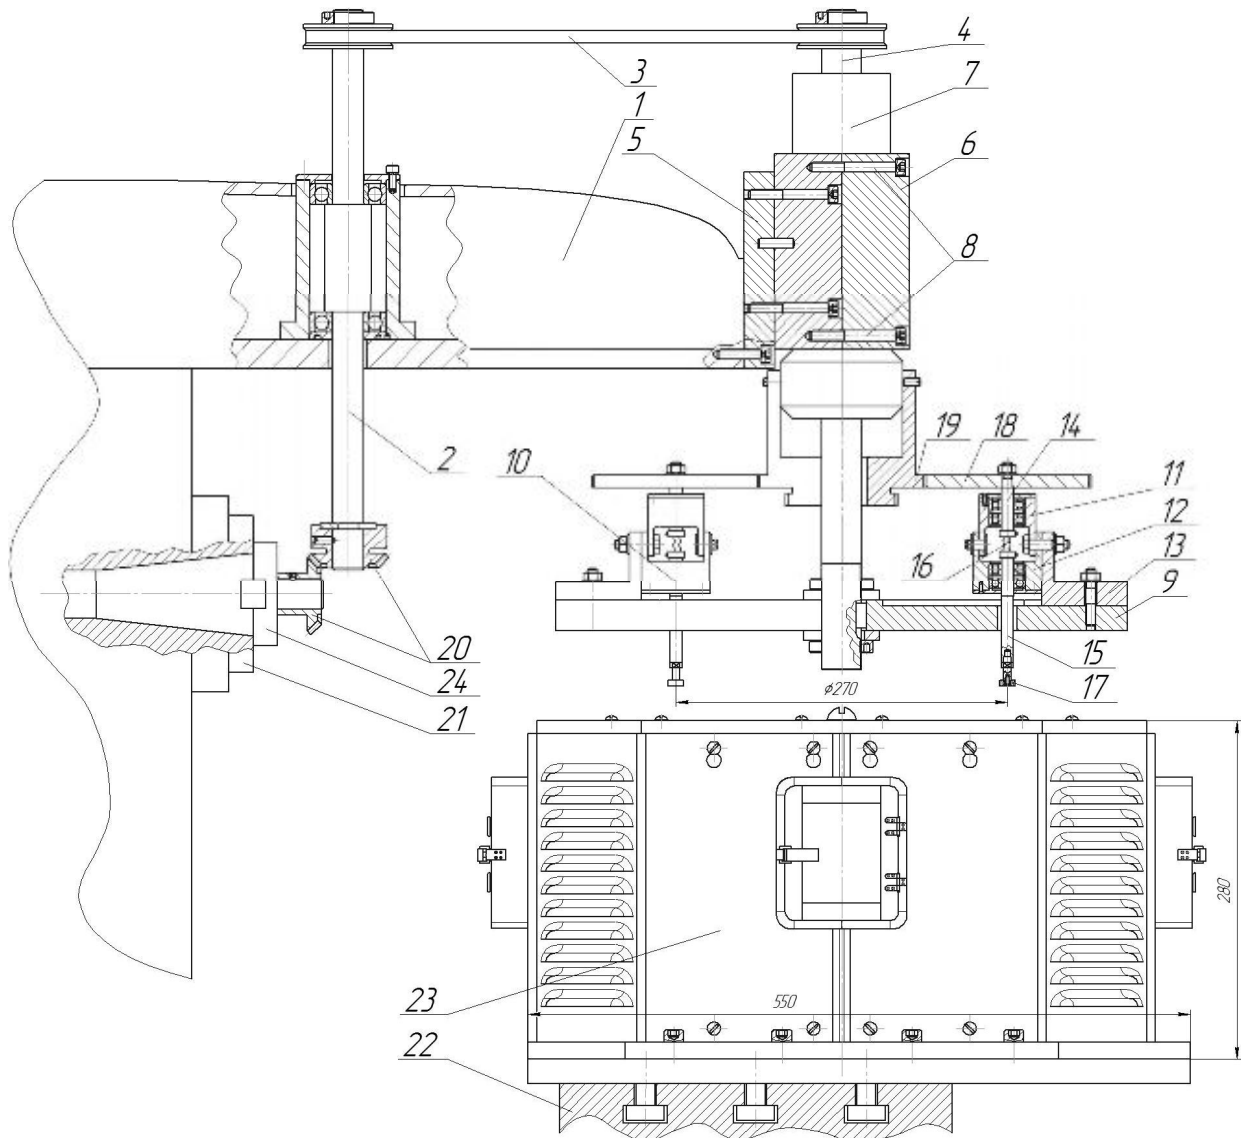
Модернизированный горизонтально-фрезерный станок для МАО
